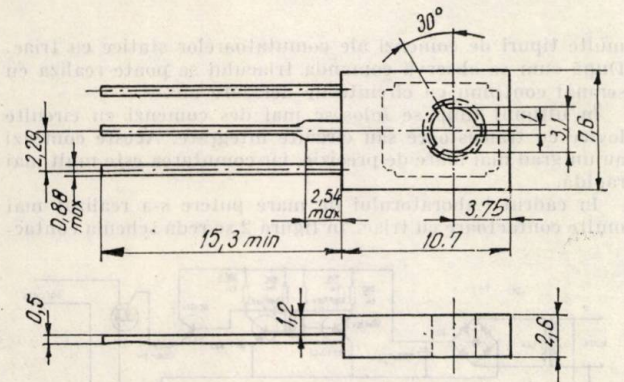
Desen de ansamblu al capsulei SOT-32 (dimensiunile în mm).
